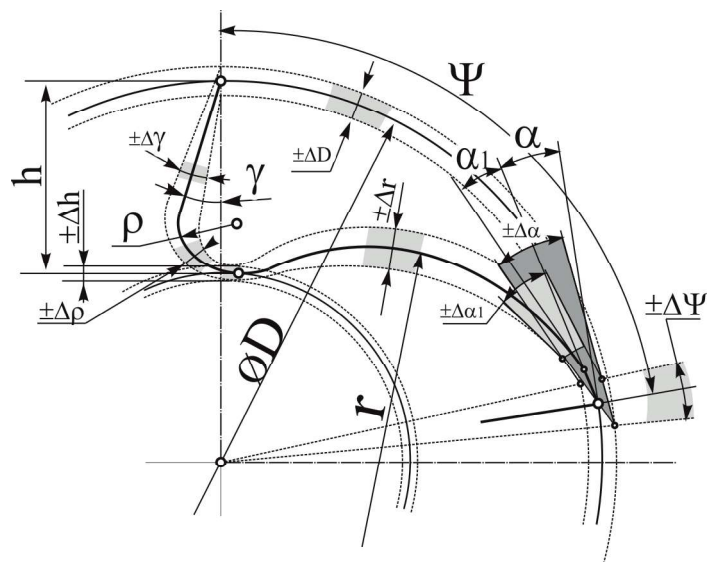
Схема построения поля допуска на профиль винтовой стружечной канавки концевой фрезы
